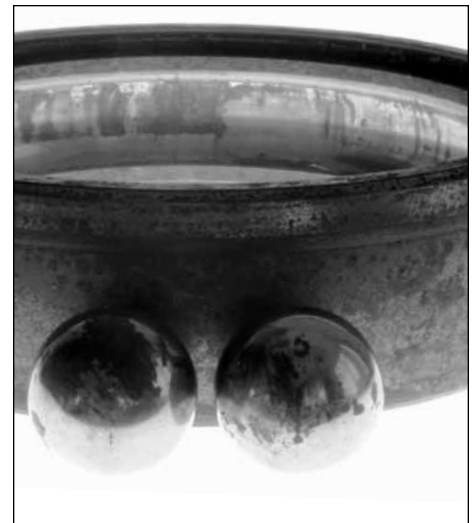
El anillo interior del rodamiento cilíndrico presenta signos de manchado y corrosión.
